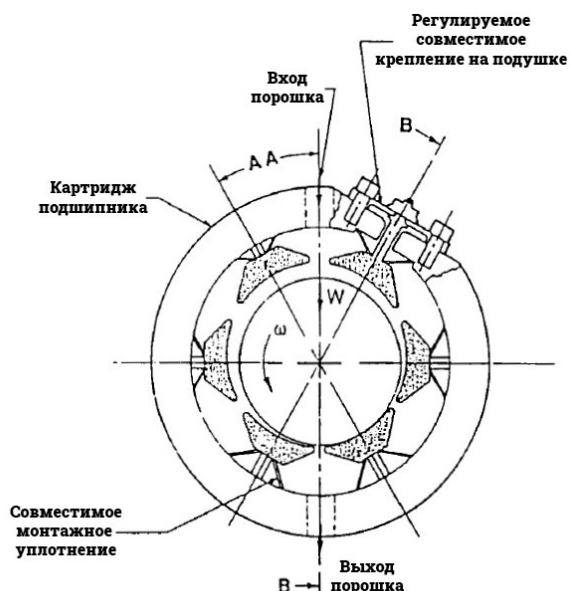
Схема сегментного подшипника с порошковой смазкой
